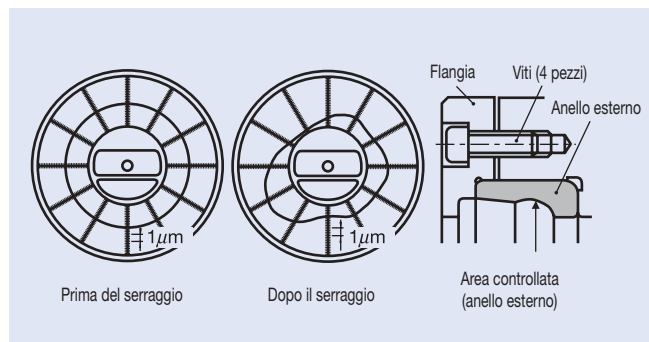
Deformazione della Superficie di Rotolamento provocata da un Serraggio Eccessivo
